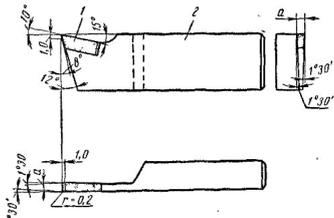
Отрезной резец с напаянной пластинкой из твердого сплава
